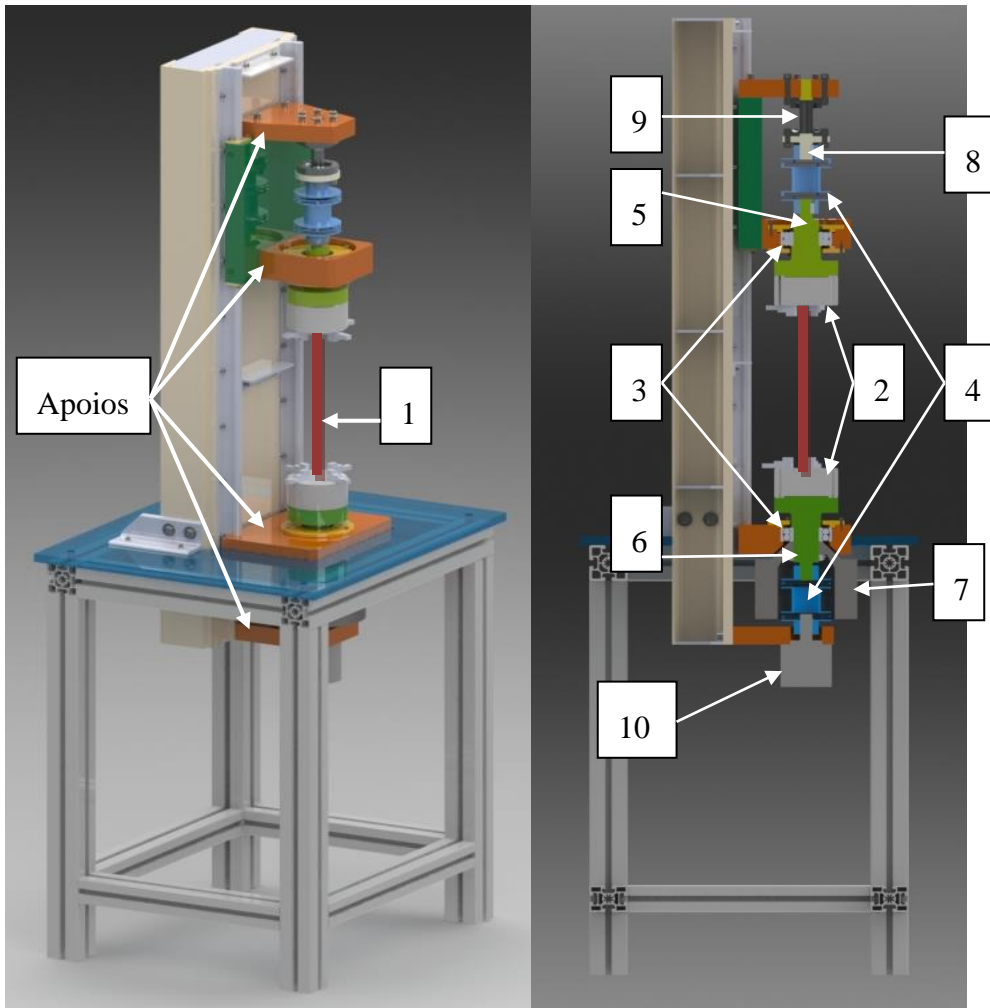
Máquina em vista isométrica (esquerda) e em corte (direita)
